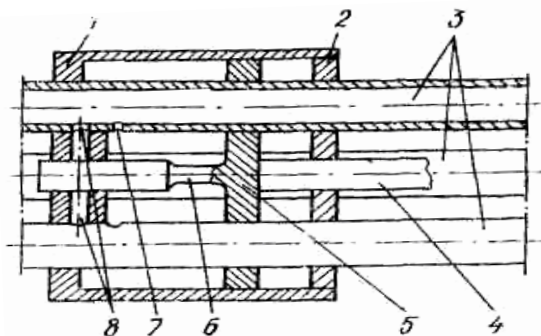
Одноциліндровий двокамерний двигун
